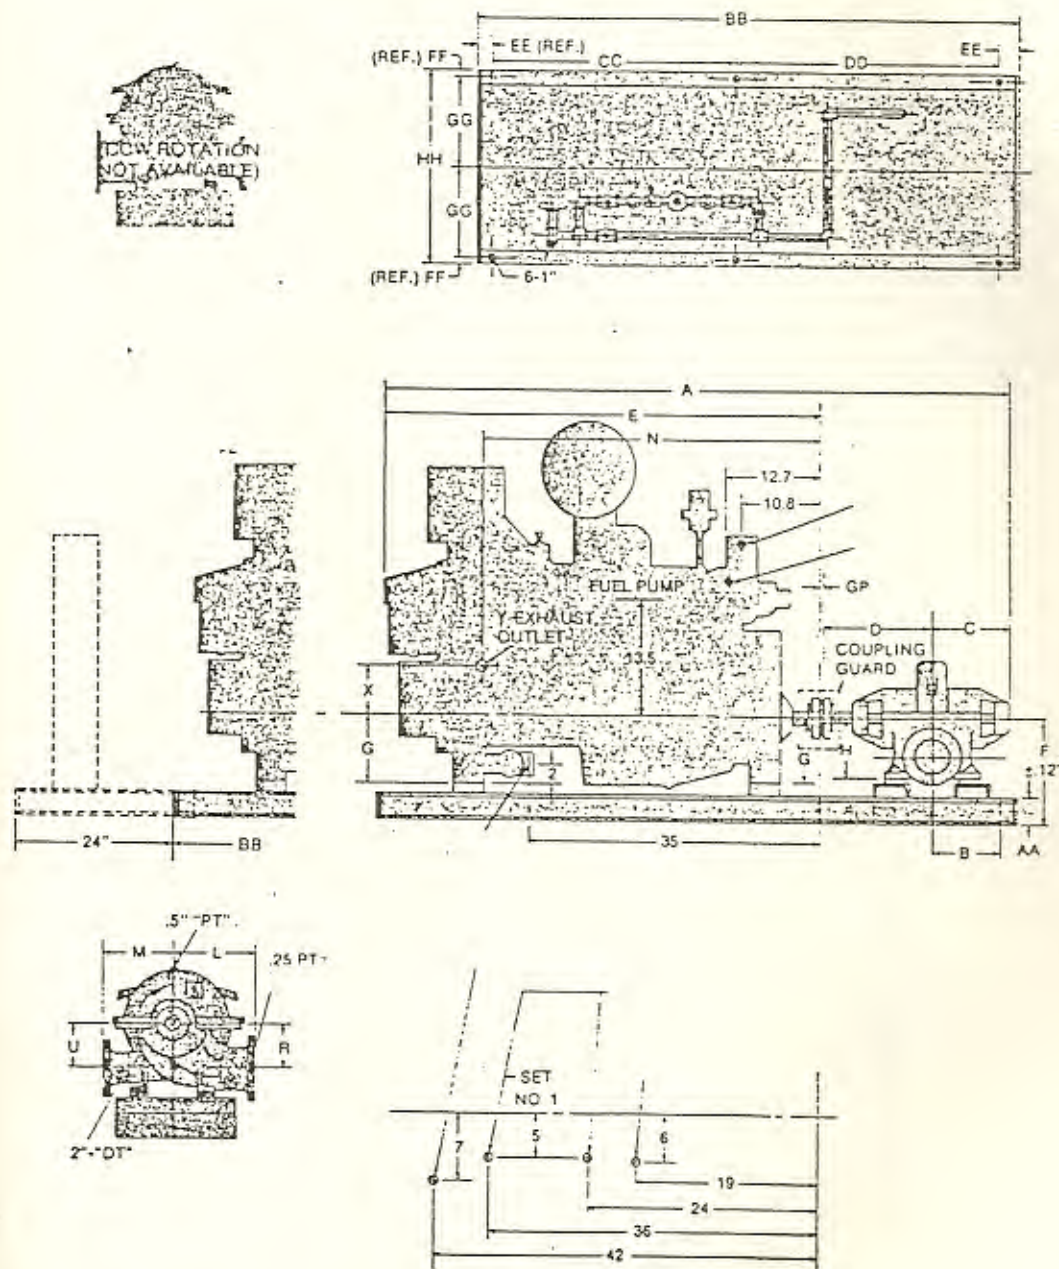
b. Dimensiones Conjunto Motor Diesel - Bomba
